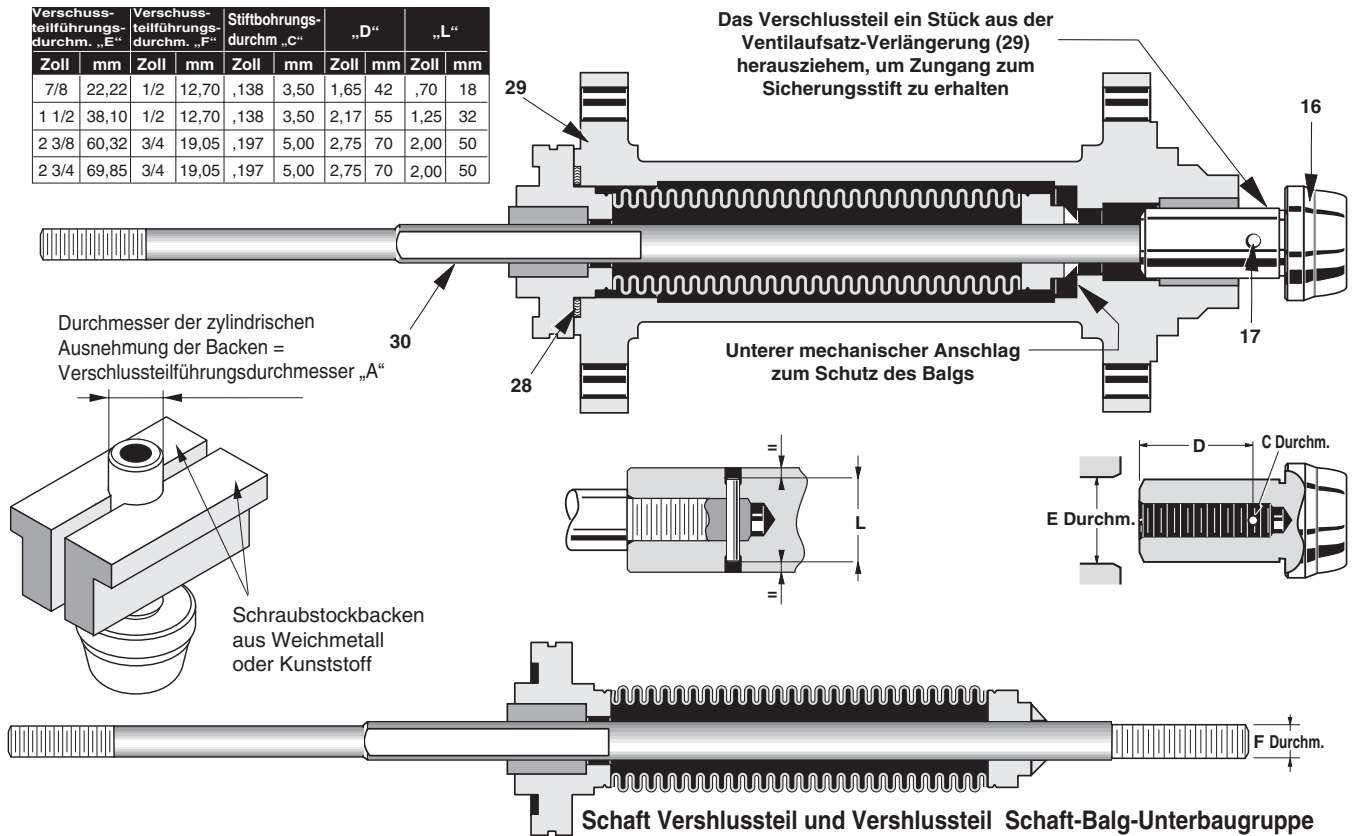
Entfernen und Einsetzen des Sicherungsstifts für die Befestigung des Verschlussstücks am Schaft
